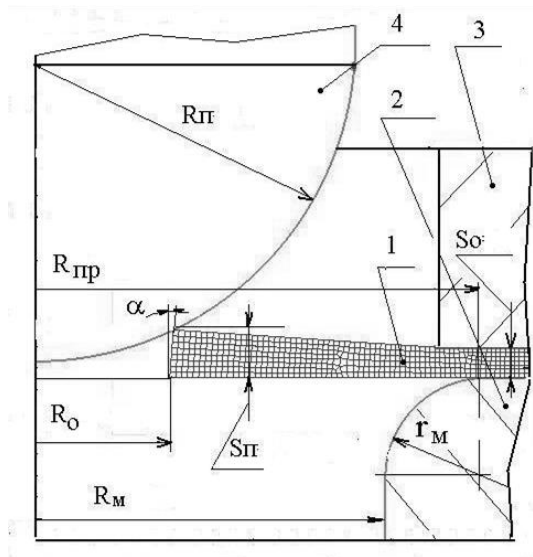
Розрахункова схема відбортуння зпрофільованої заготовки
